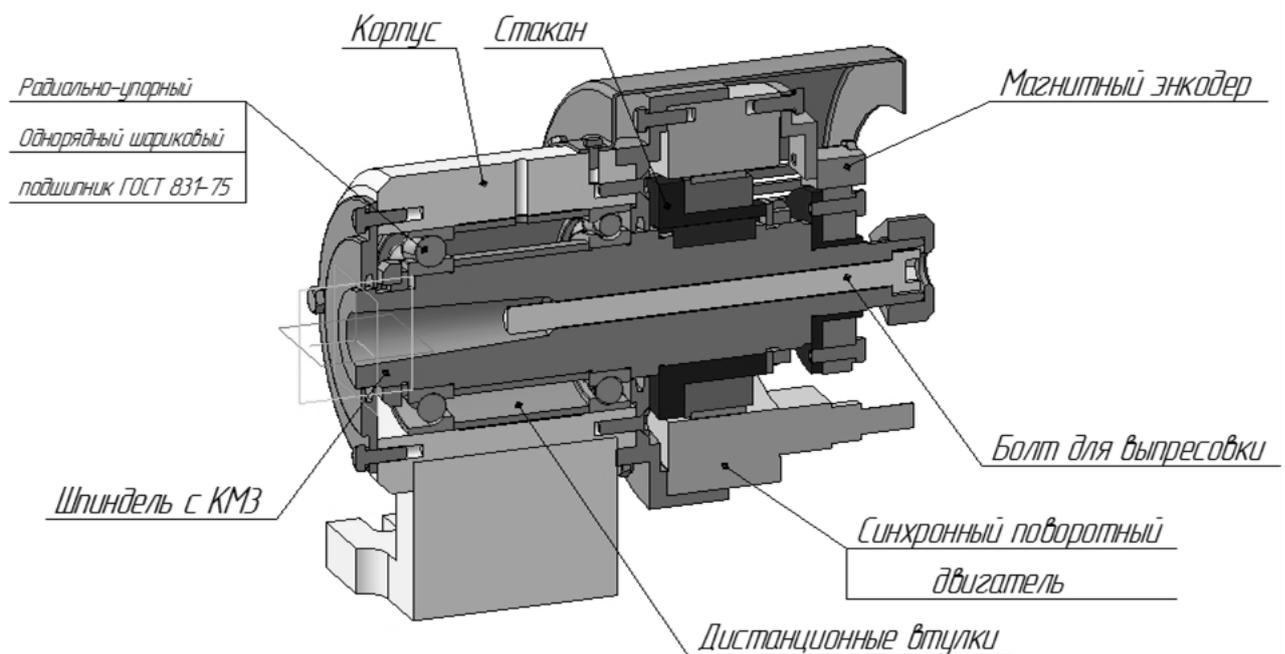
Разрез 3D модели бабки шлифовально-заточного станка с ЧПУ
